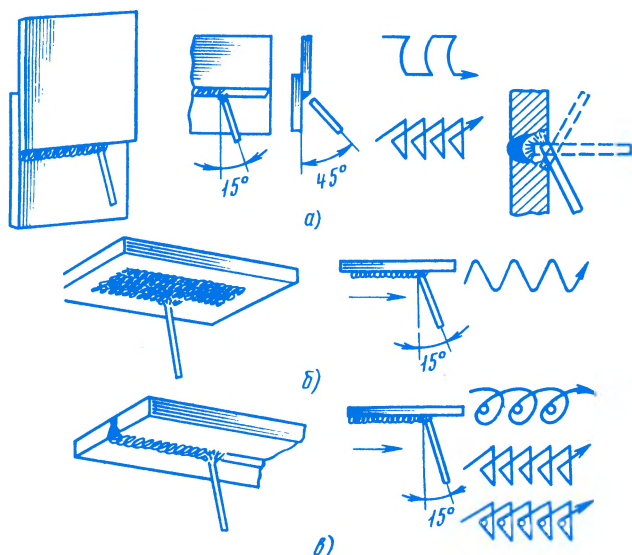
Положение и движения электрода при сварке в горизонтальном и потолочном положениях:
